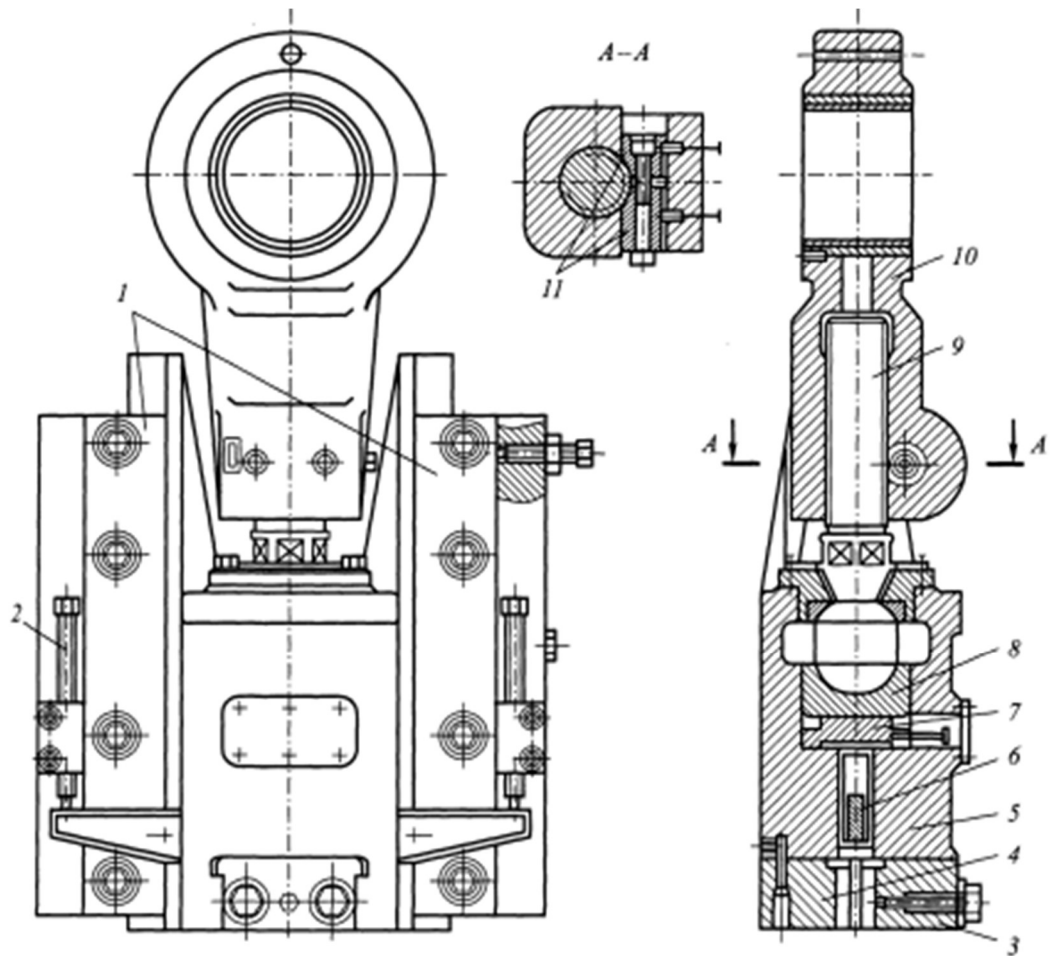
Конструктивна схема механізму регулювання висоти повзуна одного кривошипного преса
